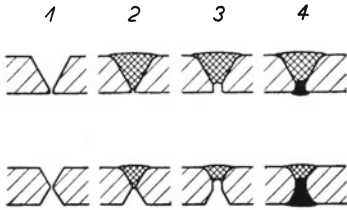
Herstellung elektrisch und autogen geschweißter Nähte.
